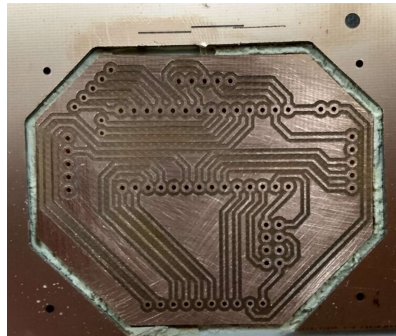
Primera etapa de soldadura del PCB de sensores ultrasónicos.
